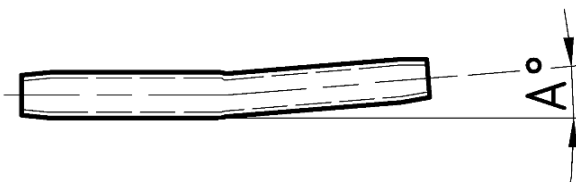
Общий вид нижней выравнивающей пластины.
